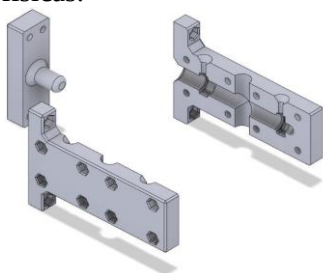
Exemplar de projeto de molde para componente elastomérico.
